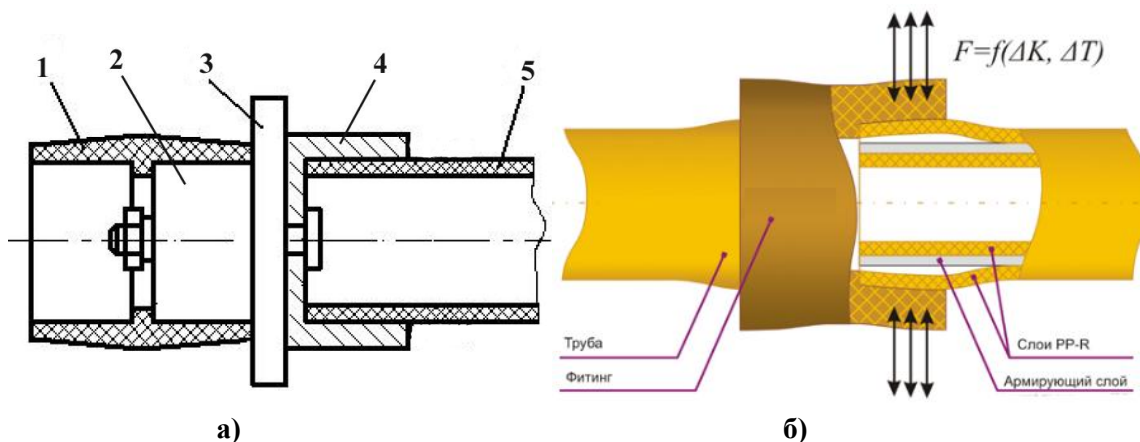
Схеми зварювання композитних труб нагрітим інструментом врозтруб (а) [18] та руйнування розтрубного зварного з'єднання (б) [19]: 1 – муфта; 2 – дорн; 3 – пластина нагрівального інструменту; 4 – гільза; 5 – труба
